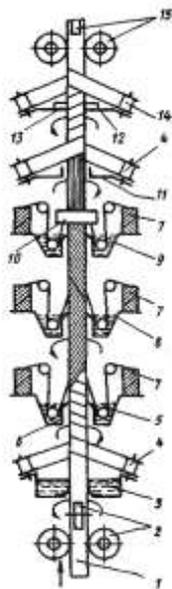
Схема вертикальной установки для формования труб на движущейся оправке
